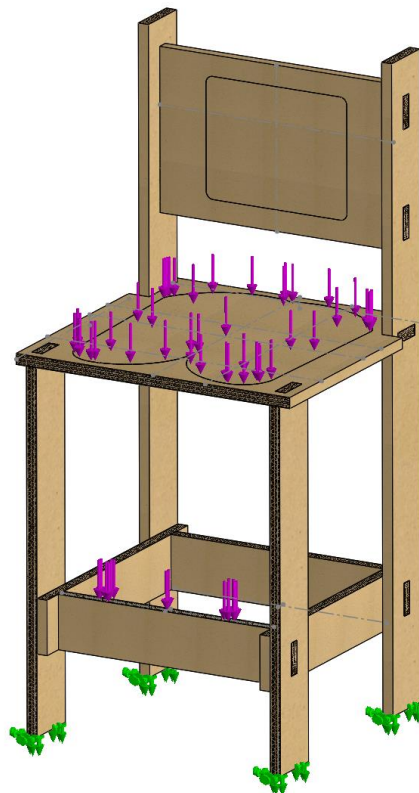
Configuración ensayo de carga estática sobre la barra de apoyo para los pies ||
